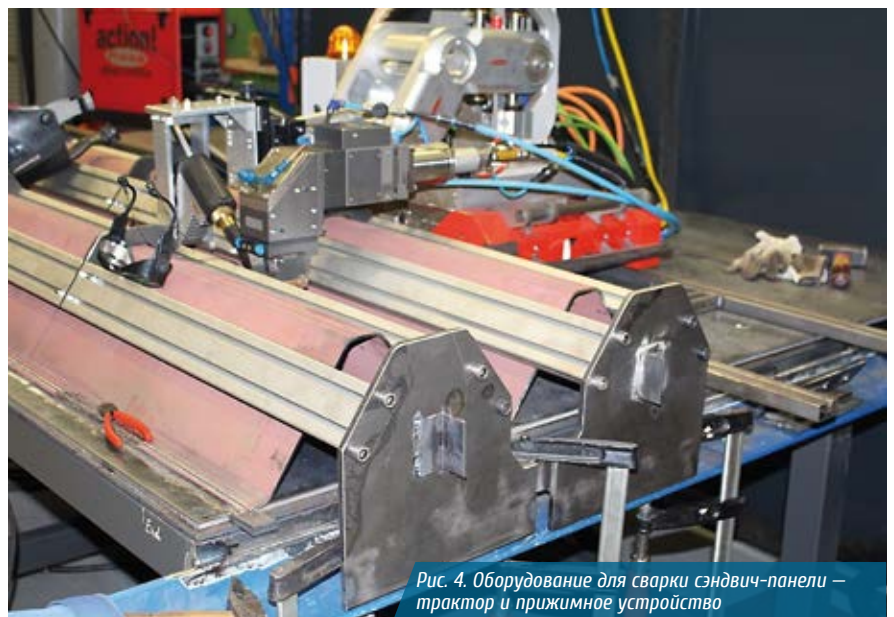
Оборудование для сварки сэндвич-панели — трактор и прижимное устройство
